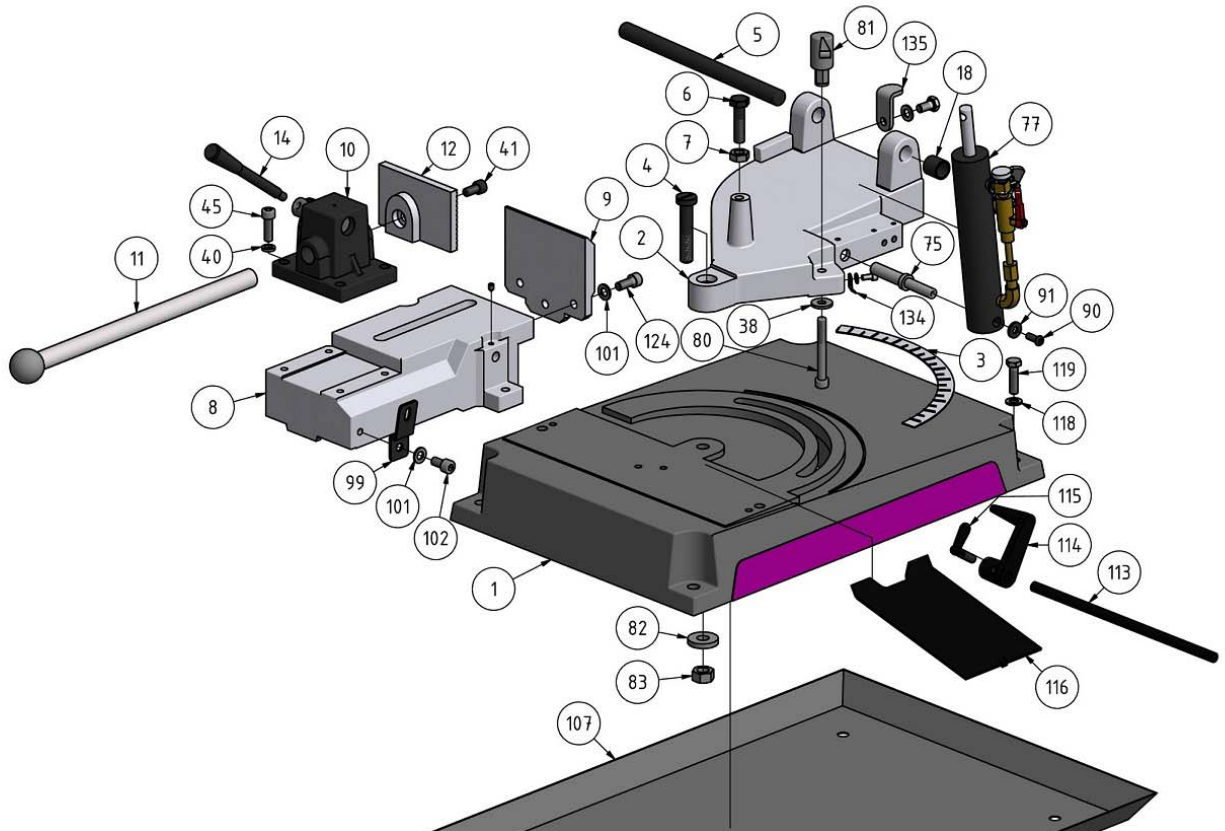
Ersatzteilzeichnung 3 von 4 - Parts drawing 3 of 4
